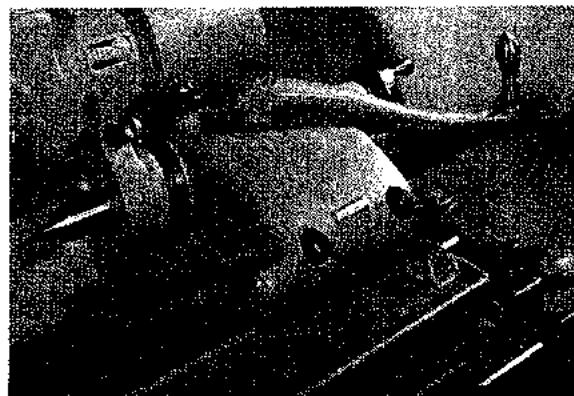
Contracabezal de una rectificadora cilíndrica (Cincinnati Milling Machine Co.)
